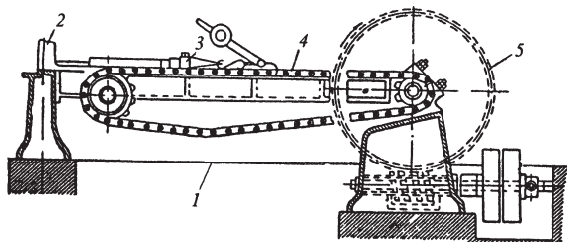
Схема волочильного стана цепного типа: 1 – стан; 2 – волока; 3 – волочильная тележка; 4 – цепь; 5 – привод волочильной тележки
